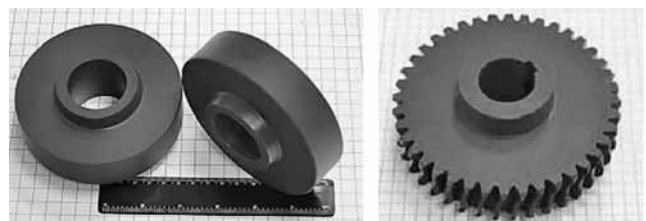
Заготовки для зубчатых колес и общий вид готовых изделий
